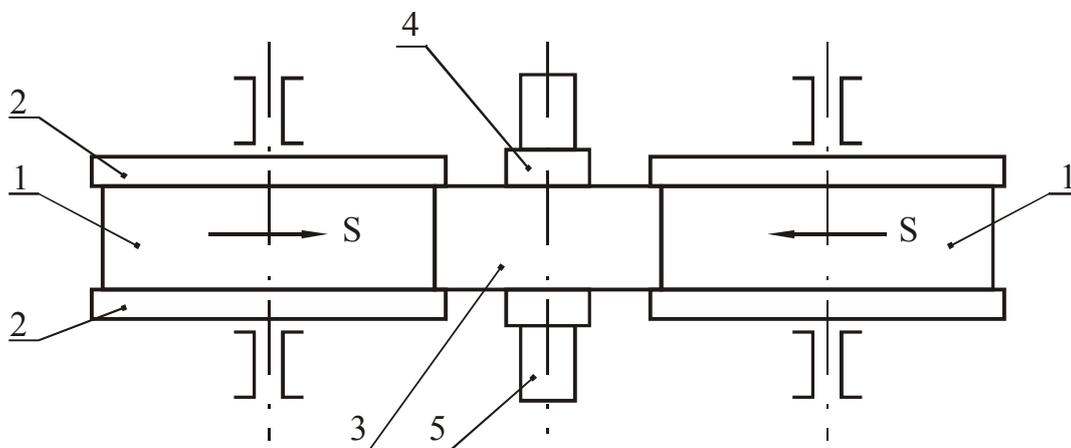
Схема горячего накатывания зубьев колес: 1 – накатники; 2 – реборды; 3 – заготовка; 4 – переходная втулка; 5 – оправка
